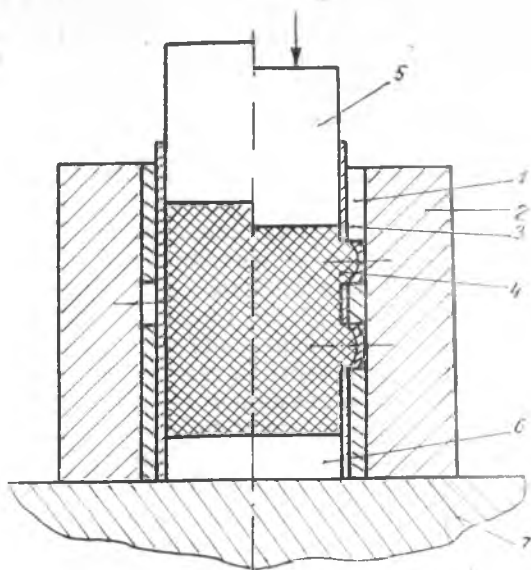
Схема пробивки полиуретаном отверстий в трубчатых заготовках
